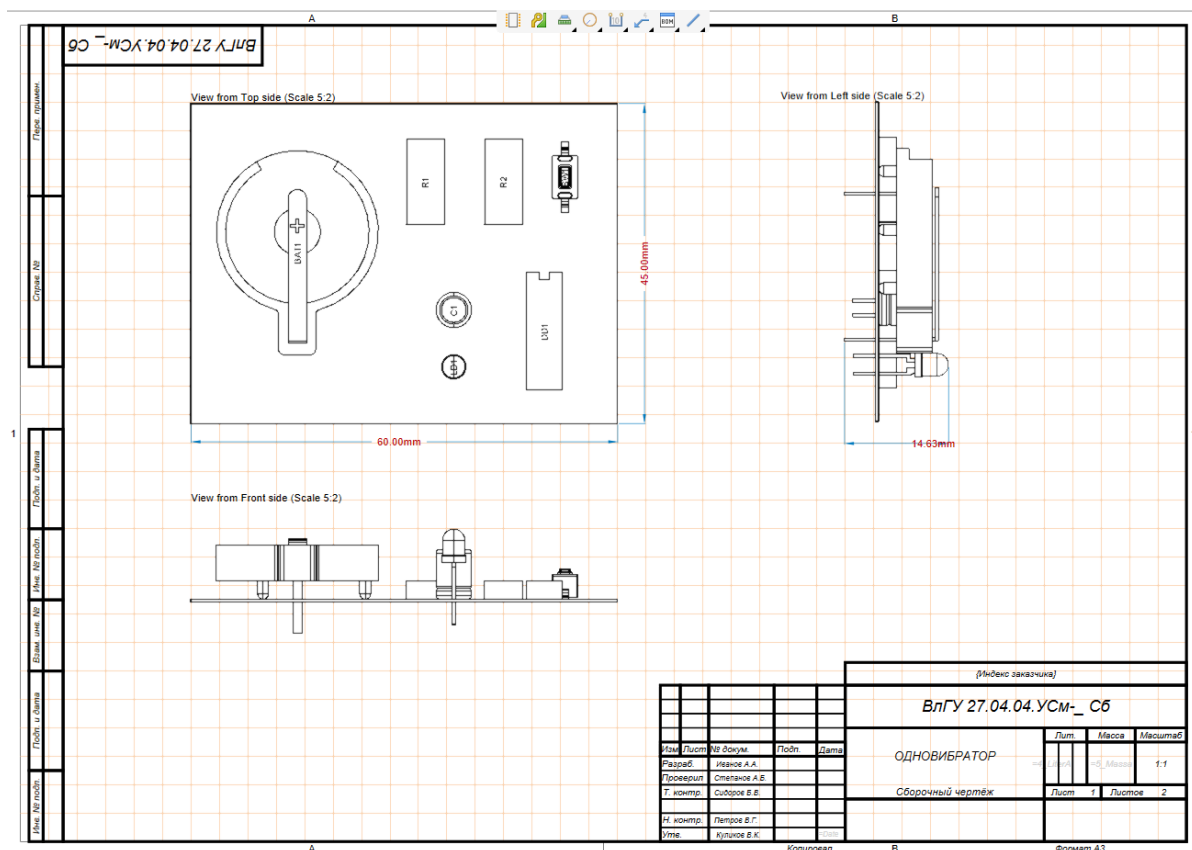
Сборочный чертеж изделия с установленными размерами
